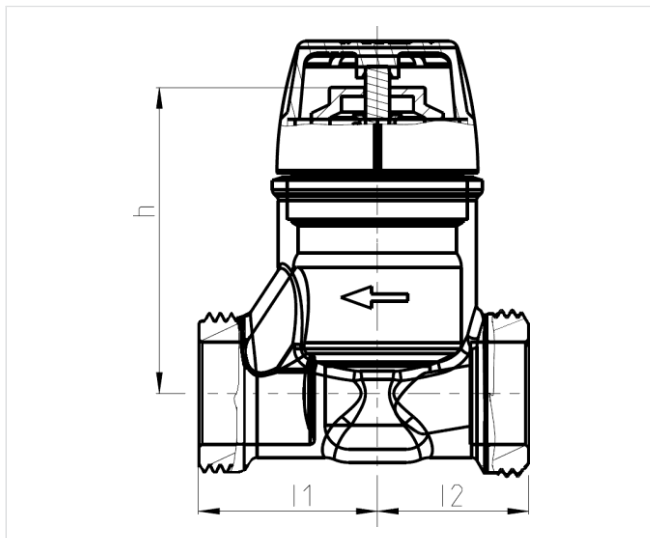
Прямой корпус с наружной резьбой и уплотнением по плоскости V2059D
